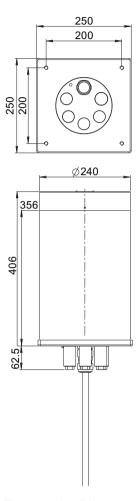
Disegno quotato modulo di campo, tutte le dimensioni in mm
